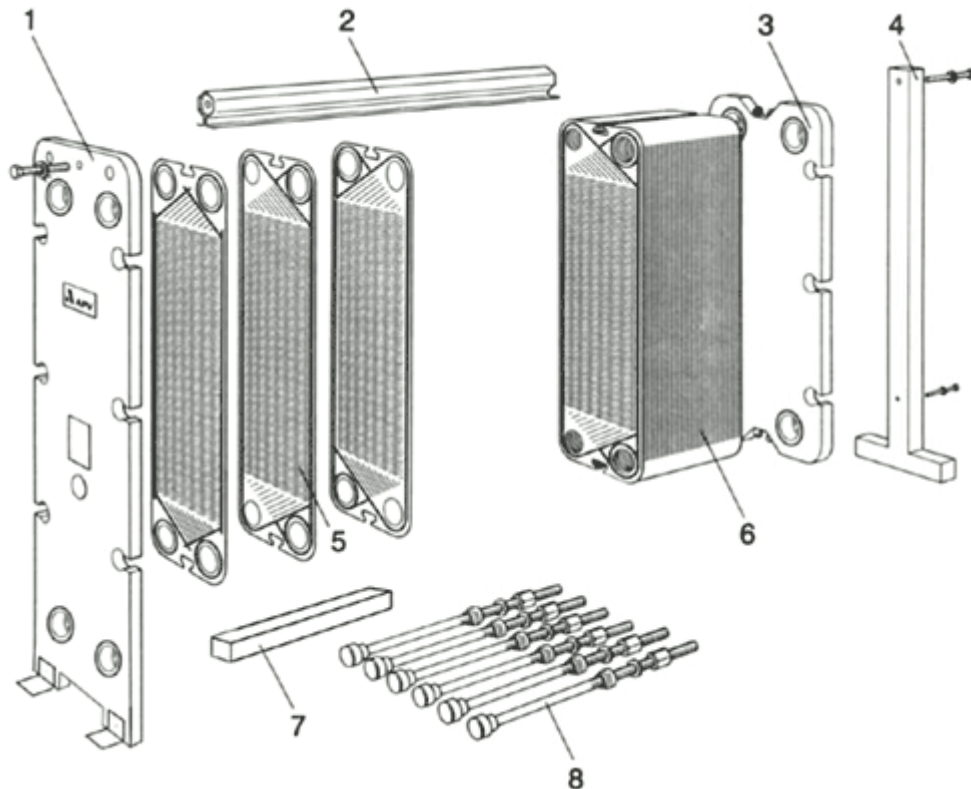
Схема пластинчастої установки: 1 – нерухома плита; 2 – верхня штанга; 3 – натискна плита; 4 – стійка; 5 – пластина з ущільнювачем; 6 – пакет пластин; 7 – нижня штанга; 8 – шпильки.
